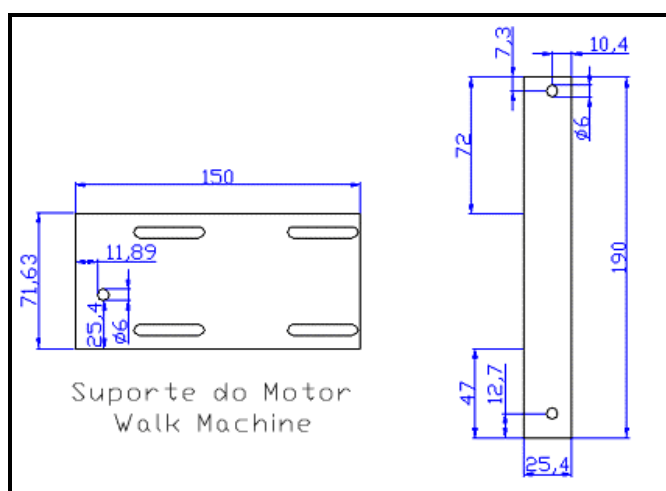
Corte do suporte do motor e soldagem na barra.
